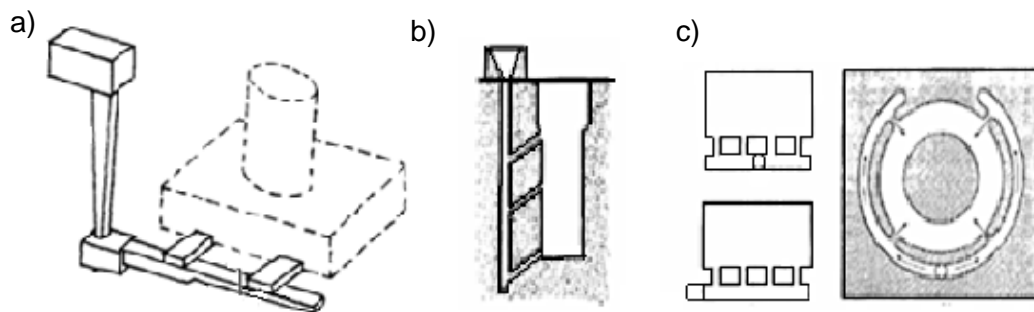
Disposición de los canales de distribución: a) Horizontal, b) Escalonado y c) Horizontal con múltiples canales de alimentación (vista en planta).
